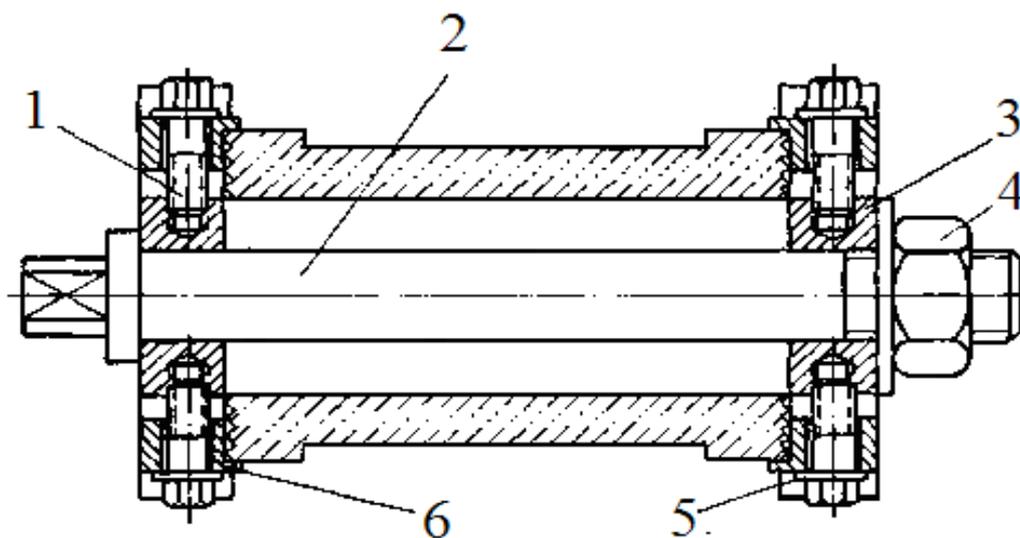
Общий вид приспособления для обтачивания наружного диаметра вкладышей:
